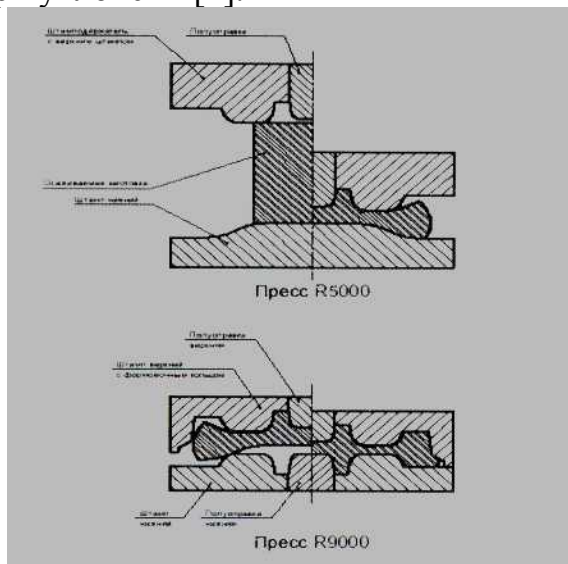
Схема деформирования заготовок железнодорожных колес.
